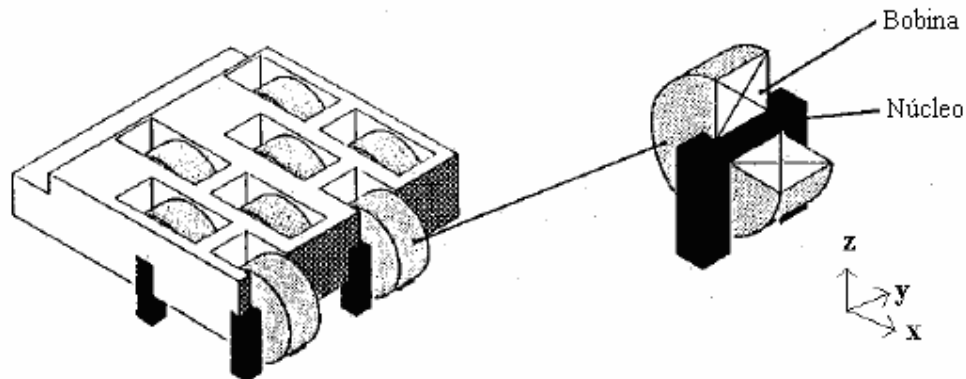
No carro do Motor de Superfície, destaque para a disposição das bobinas com os núcleos ferromagnéticos [15].
